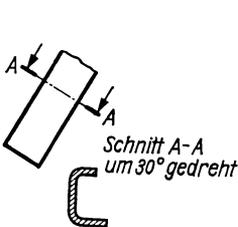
Schnittfläche, um einen bestimmten Winkel gedreht
